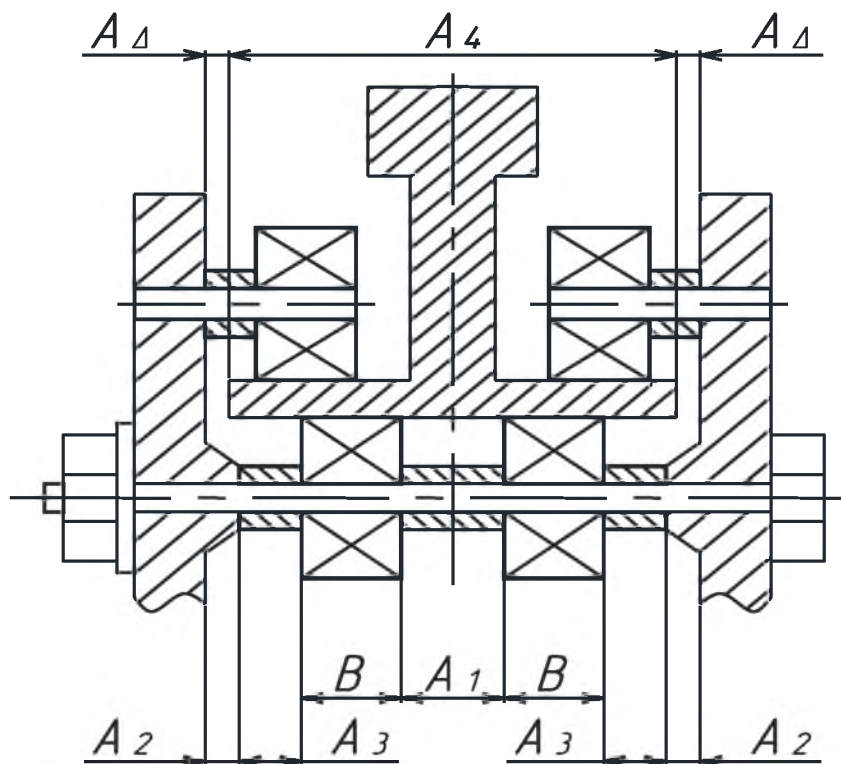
Эскиз крепления каретки выдвигного закрывка к лонжерону
